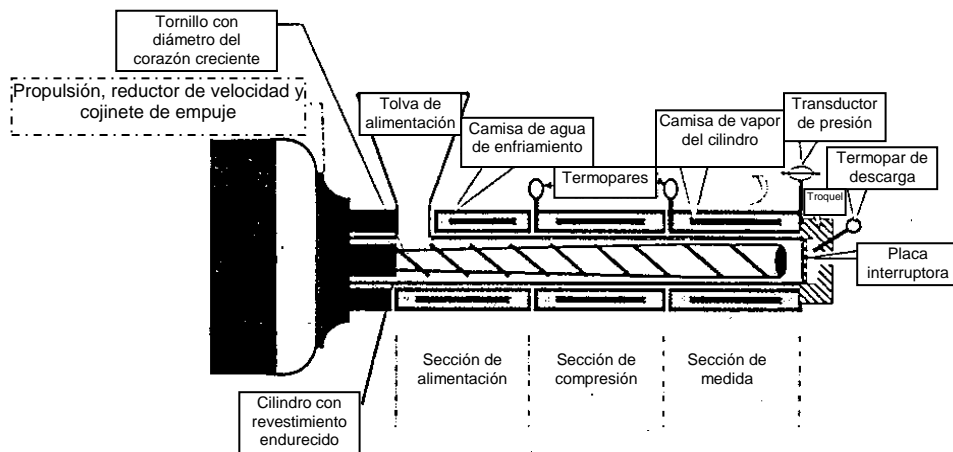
Componentes básicos del extrusor de tornillo único sólido.
